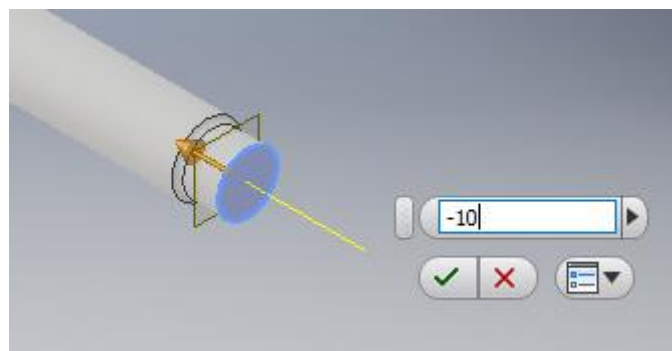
Vista detalle del indicador de distancia al plano paralelo
